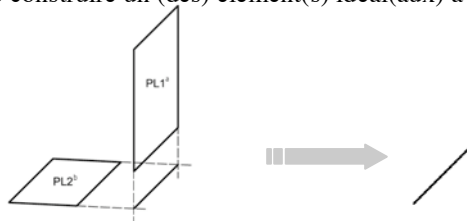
Construction : construire un élément idéal à partir d'autres éléments.
